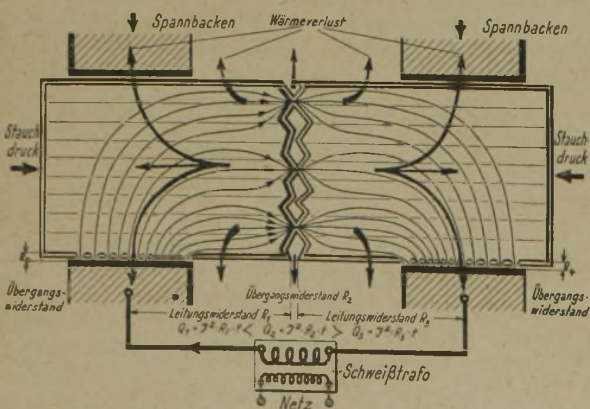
Elektrische Stumpfschweißung, Stromverlauf
